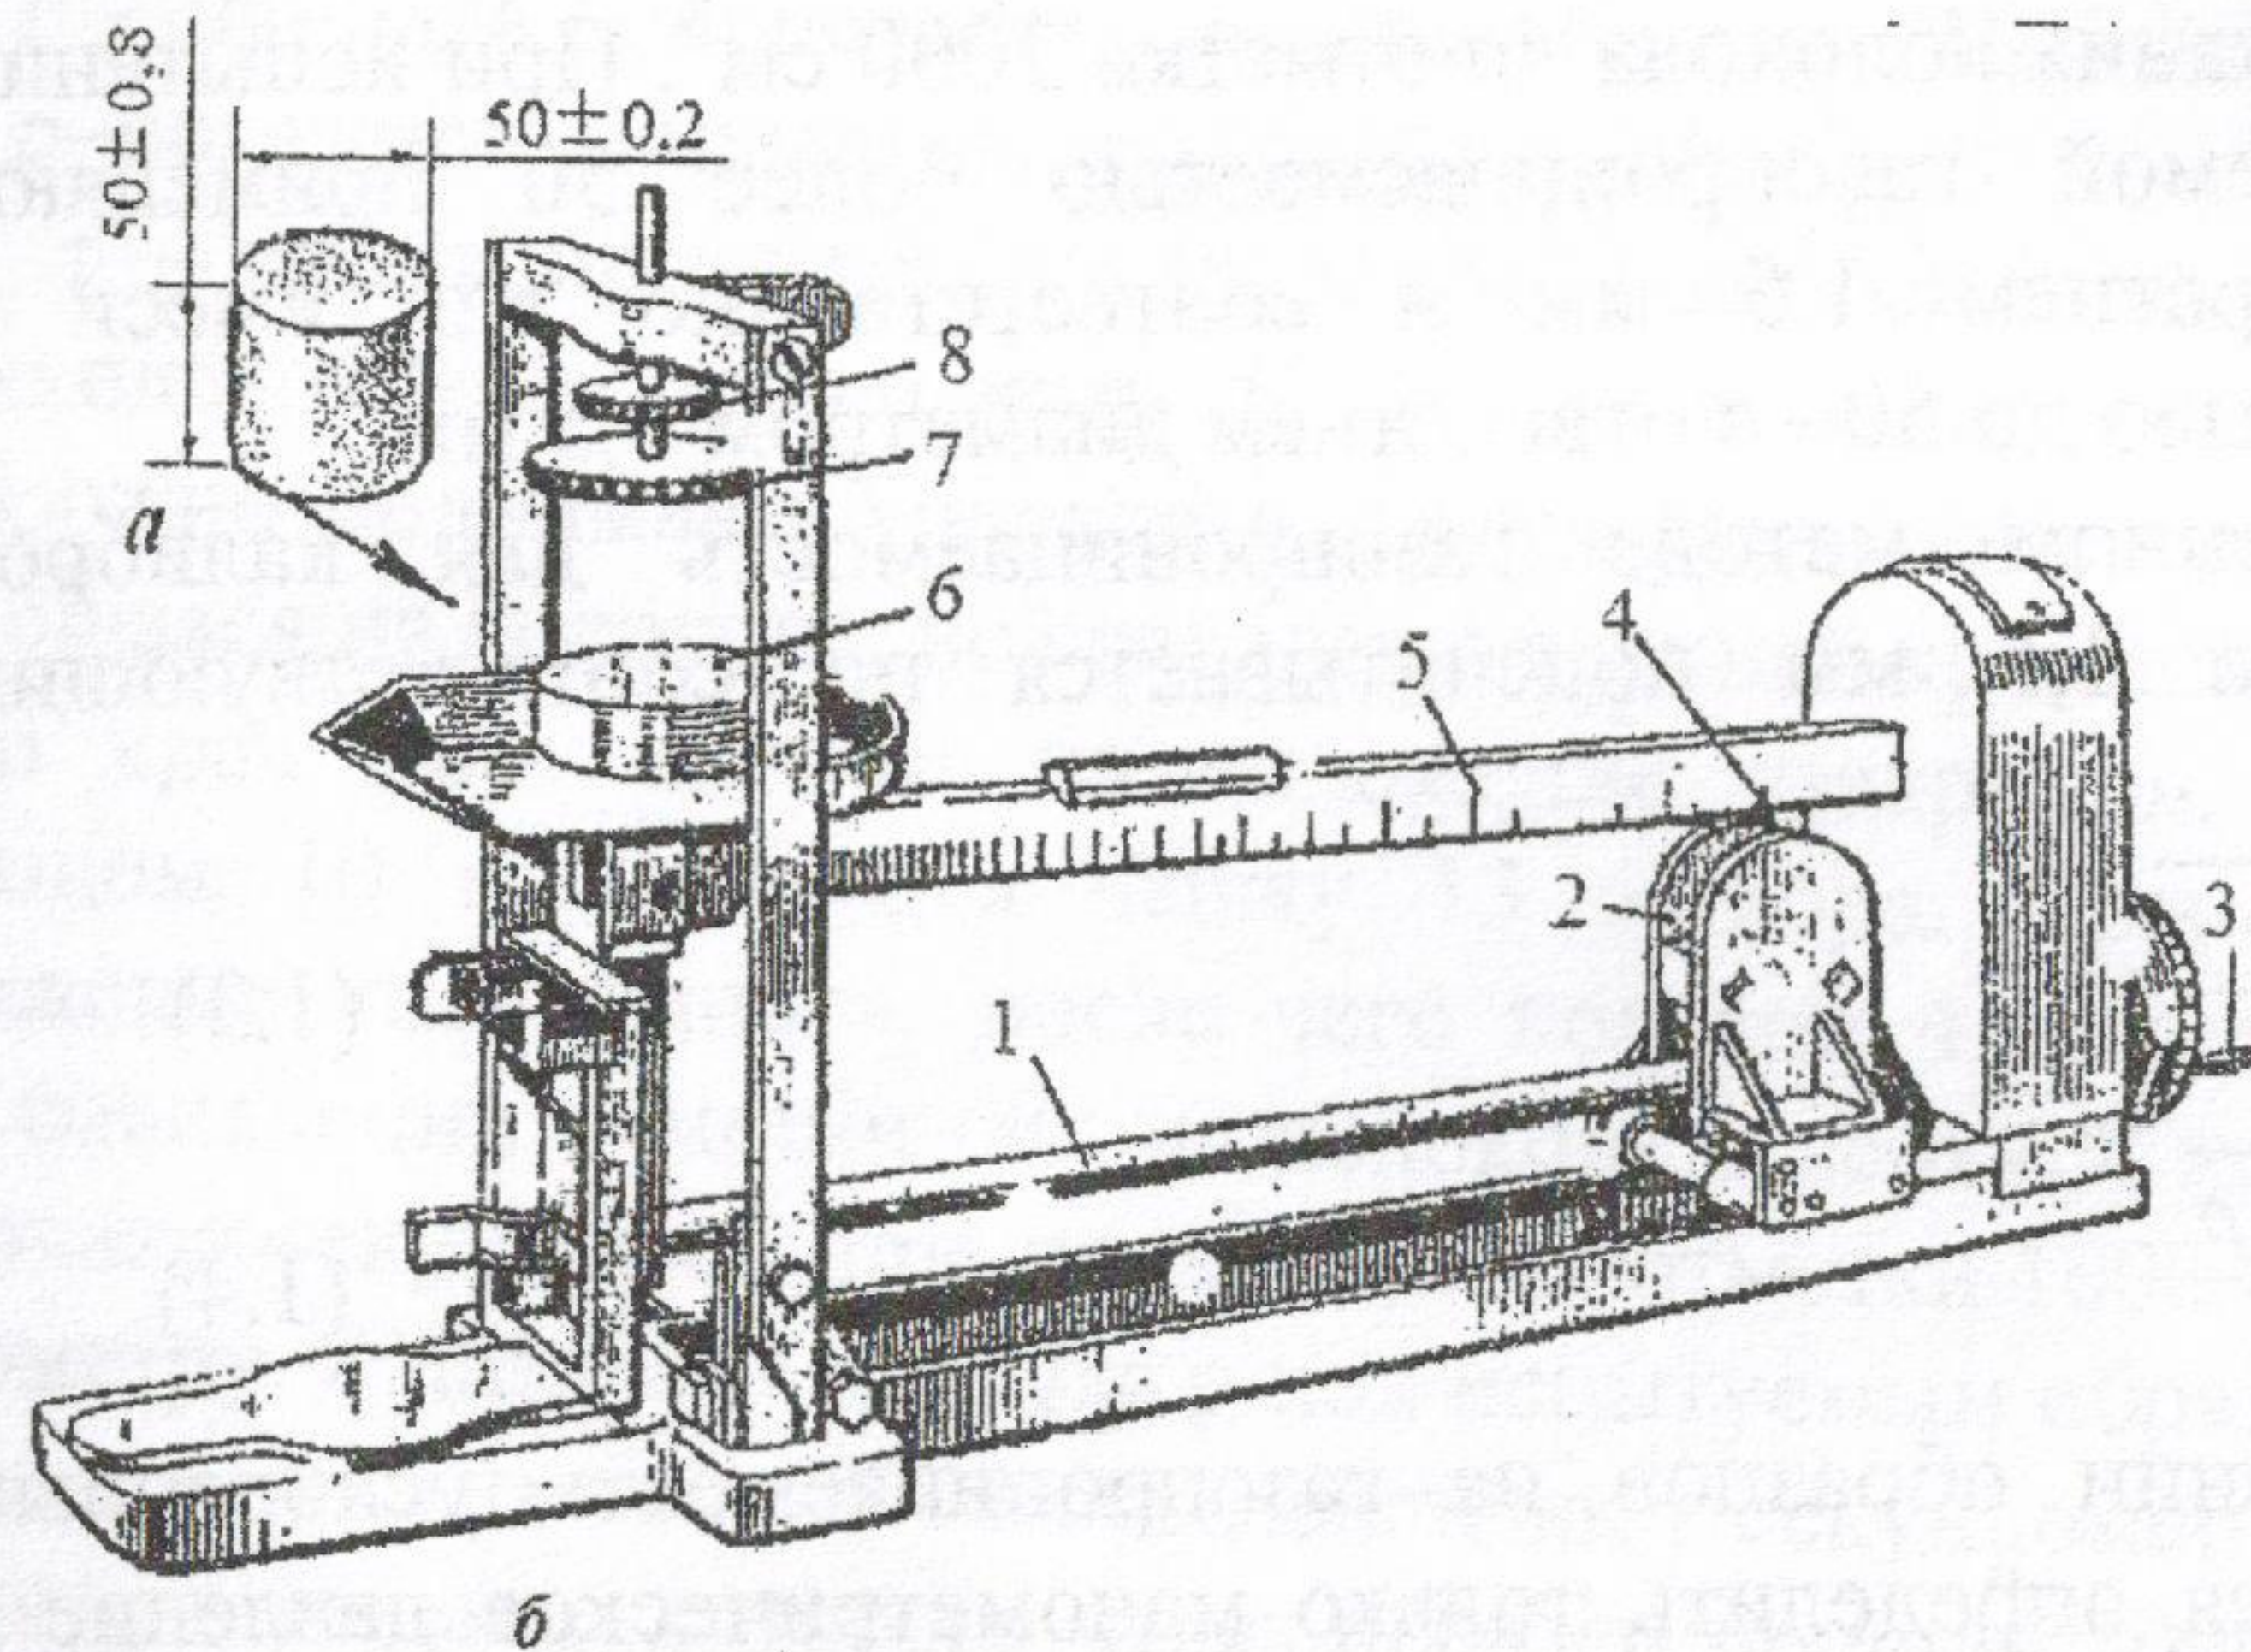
Схема испытания влажных образцов из формовочных смесей на сжатие: *a* – образец для испытаний; *б* – рычажный прибор модели 051 для определения прочности при сжатии влажных образцов: 1 – ходовой винт; 2 – каретка; 3 – рукоятка; 4 – указатель; 5 – шкала рычага; 6 – нижняя площадка; 7 – верхняя площадка; 8 – гайка
